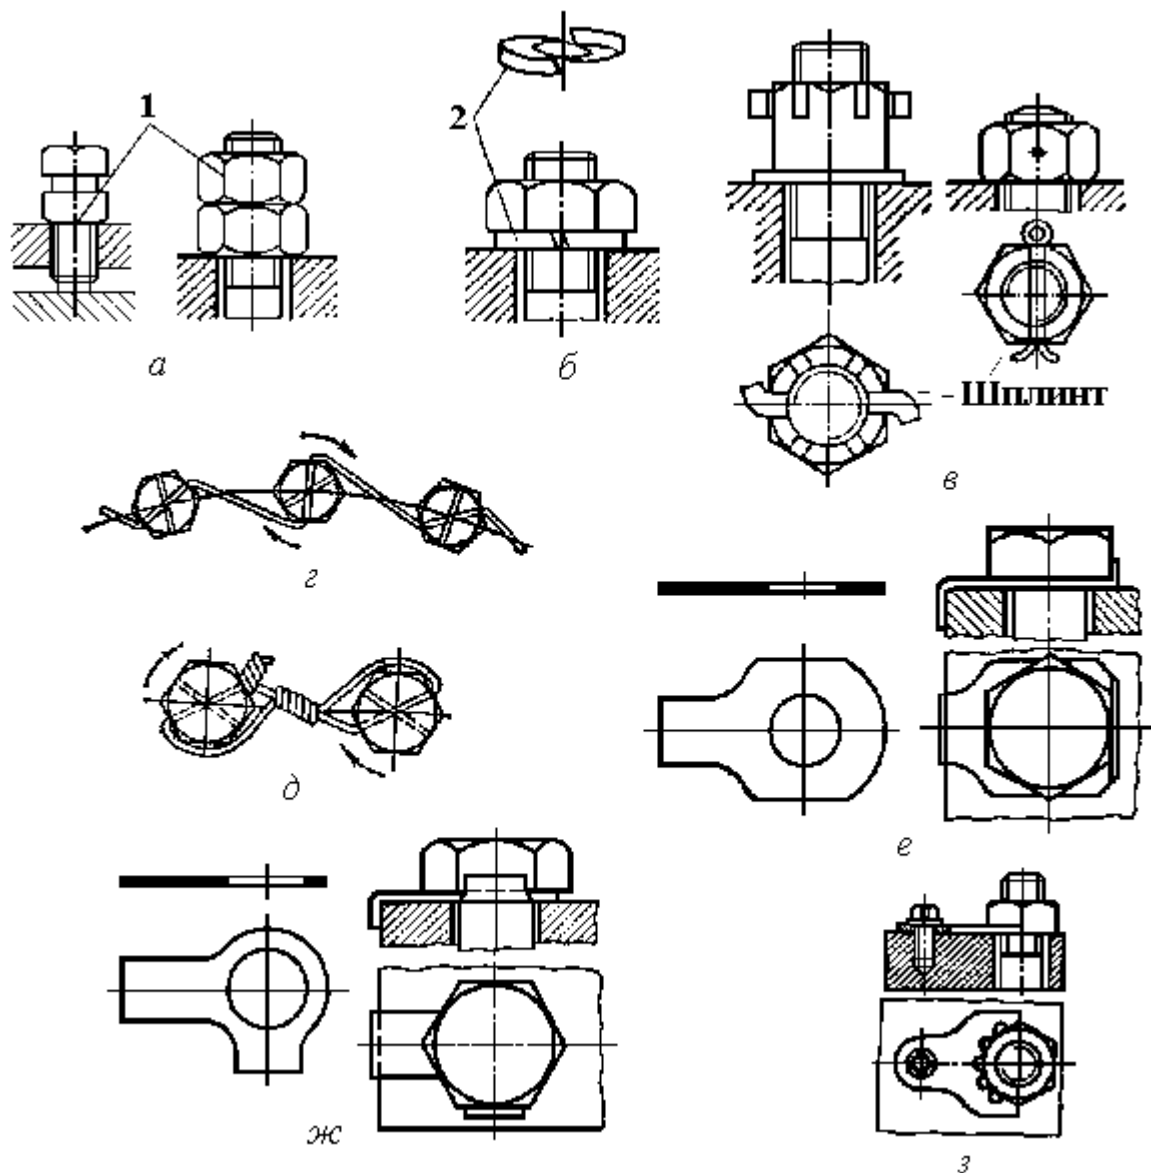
Принципы и способы стопорения резьбовых соединений
